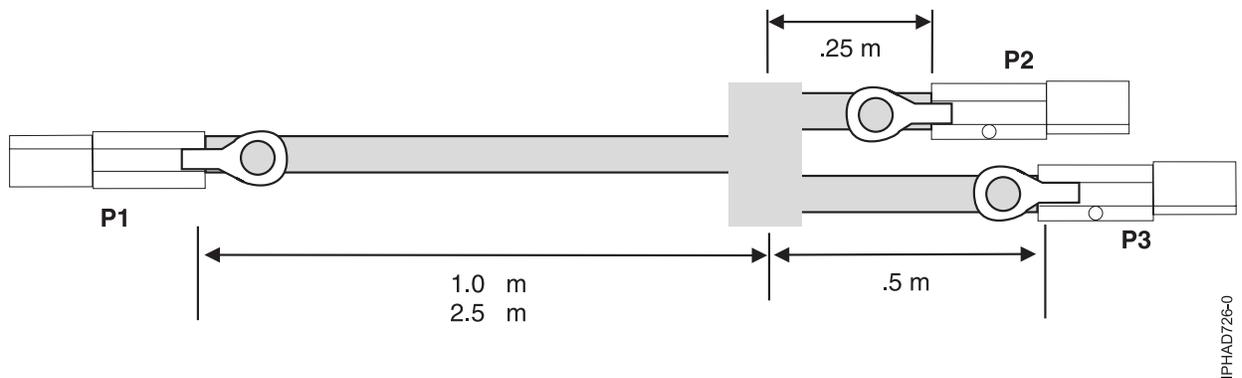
Comprimentos do Cabo do Conjunto de Cabos YI SAS Externo
